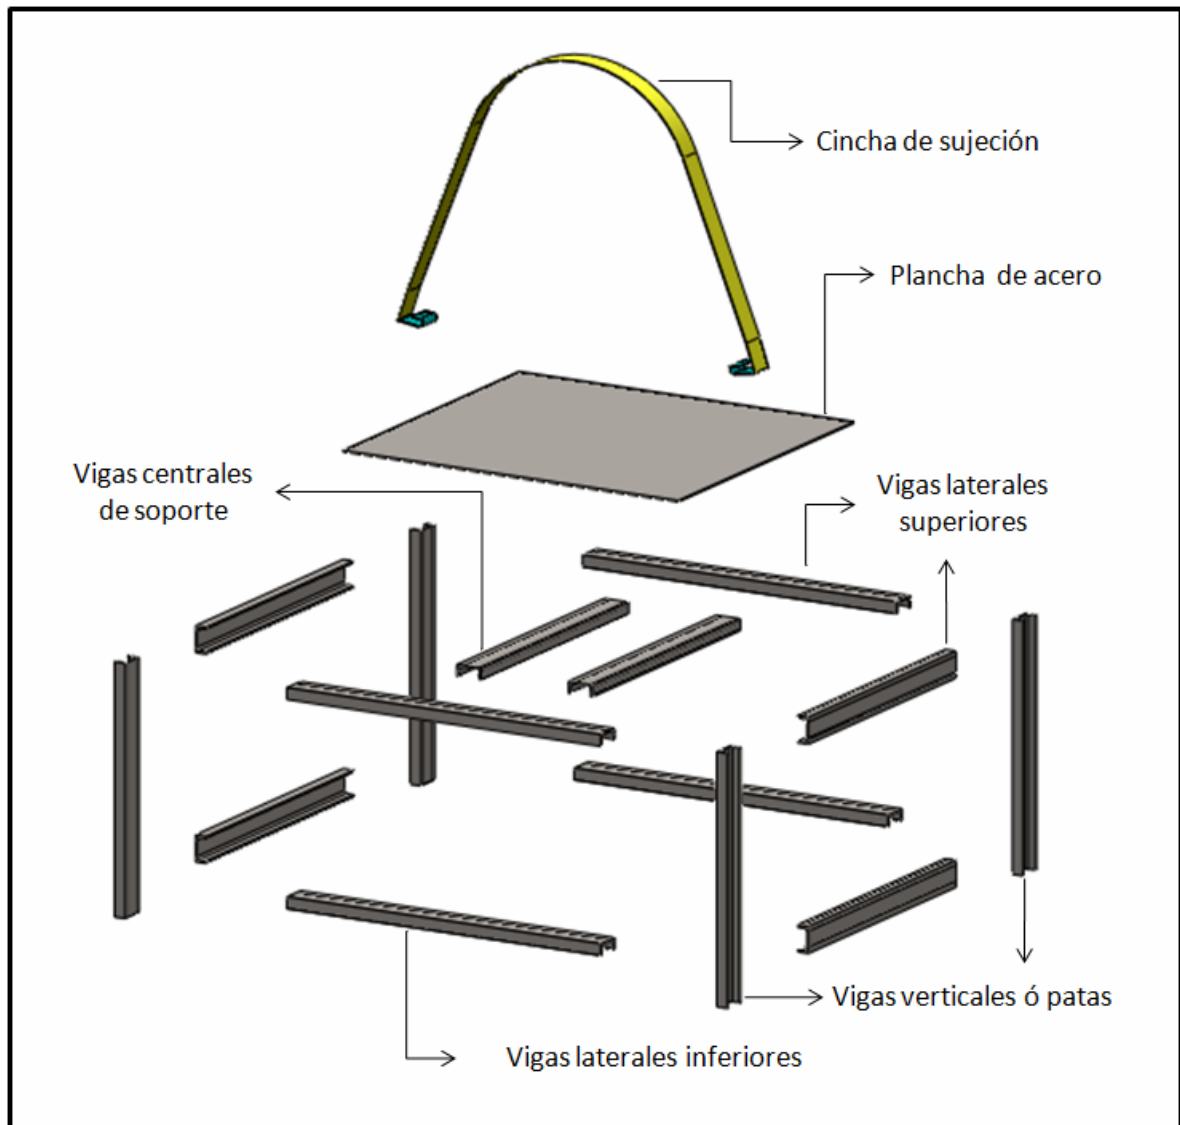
Despiece del mecanismo de sujeción del motor [Fuente: propio].
